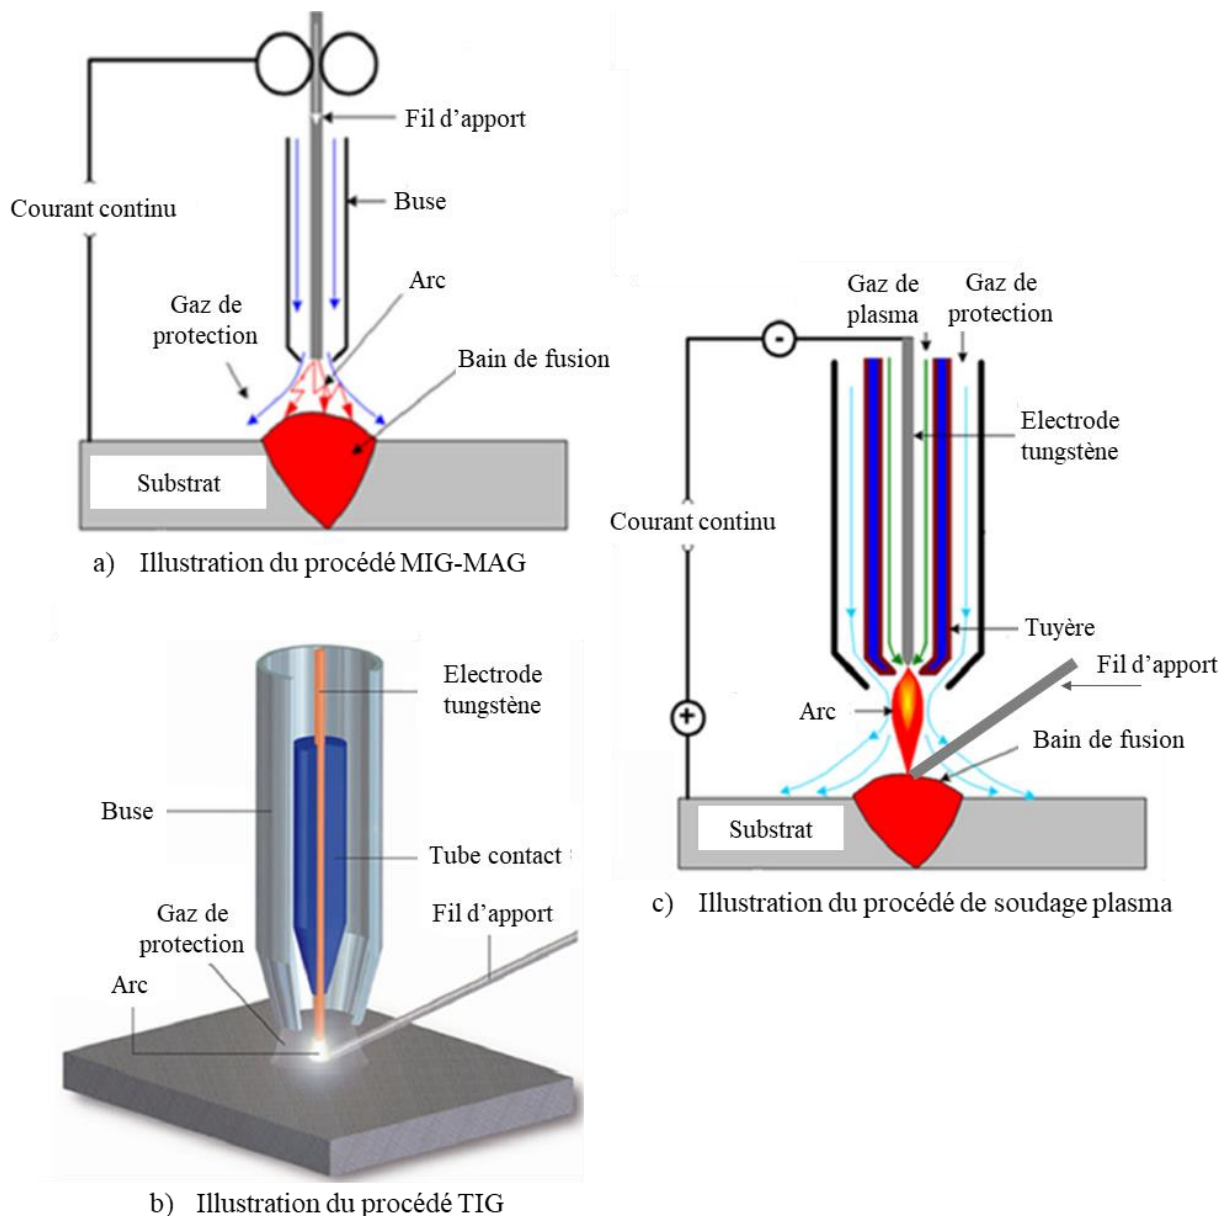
Illustration des procédés de soudage à l'arc-fil [3]
